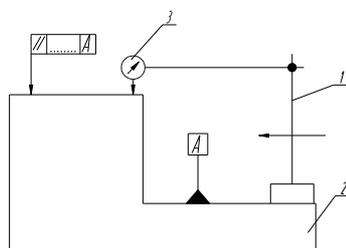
Пример измерительной базы. 1 - индикаторная стойка; 2 – изделие; 3 - индикатор (средство измерения); А - измерительная база детали.
